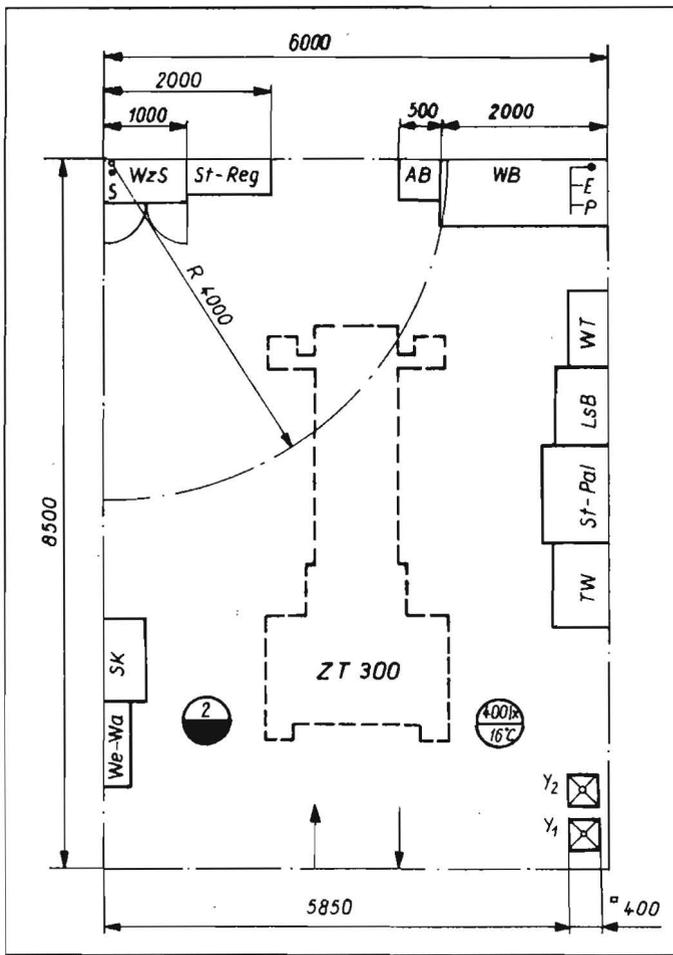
Layout des Projektbausteins „Teilinstanzsetzung ZT 300“ – Grundvariante
